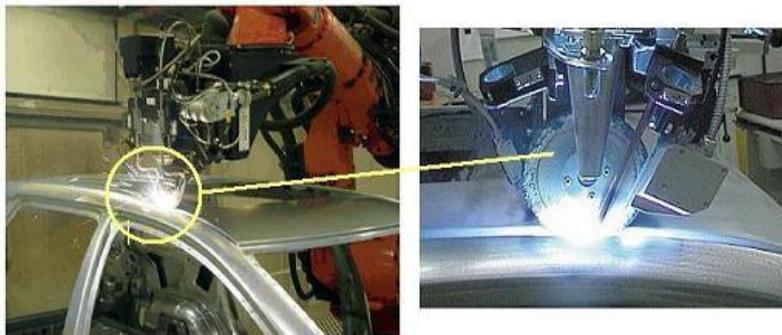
Лазерная сварка крыши автомобиля. Ролик, двигаясь впереди лазера, устраняет зазор между деталями.
